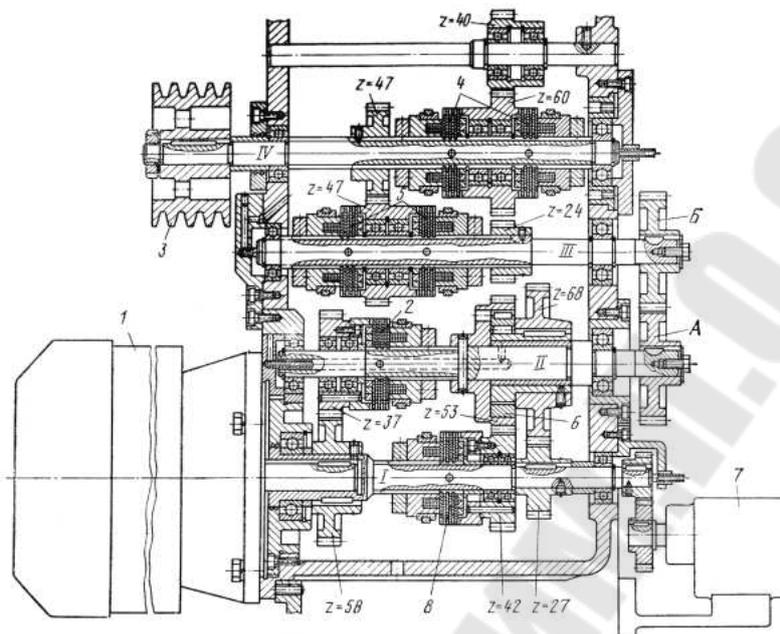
Коробка скоростей токарно-револьверного автомата:
